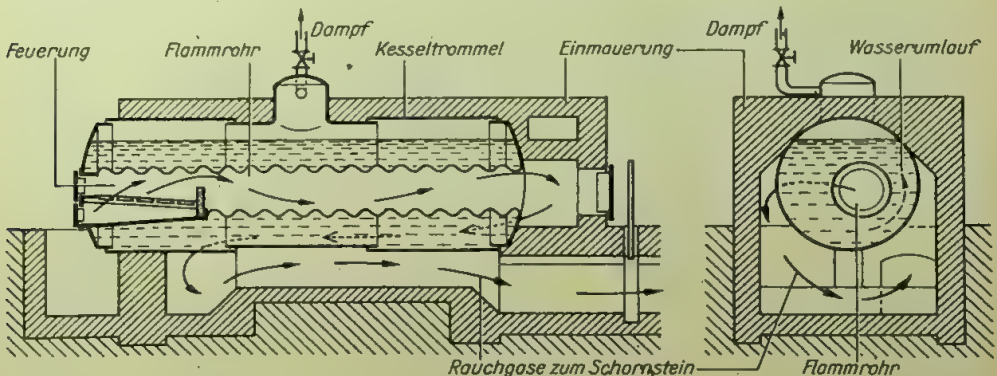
Flammrohr-Dampferzeuger
